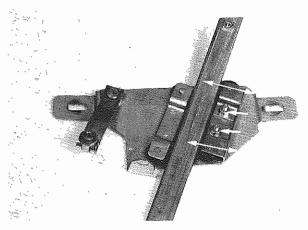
Viti fissaggio carrello mobile Screws fixing mobile carriage
